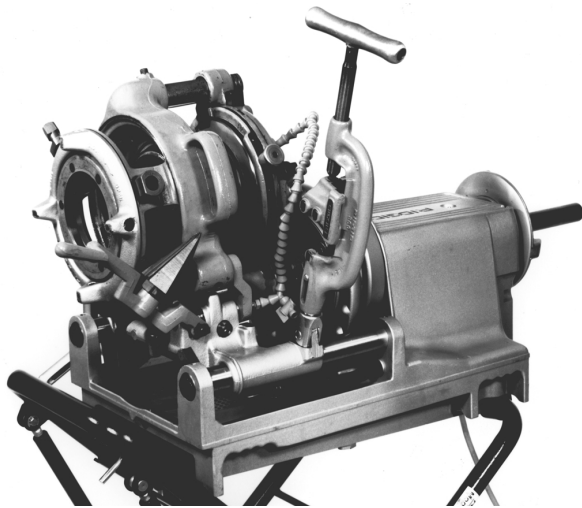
Roscadora a engranajes No. 141 montada a la No. 300 Compacta
